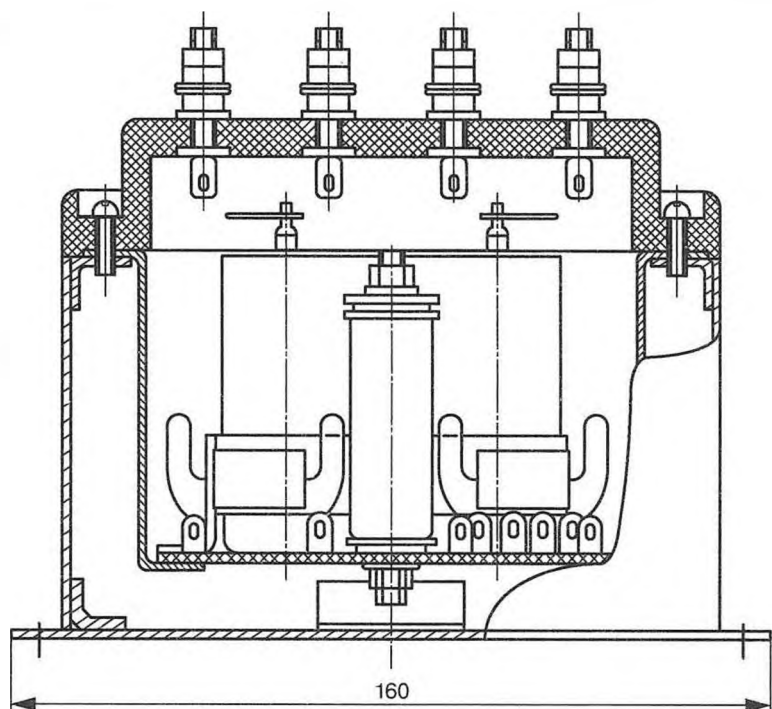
Габаритные и установочные размеры блока конденсаторного KB-4x4
